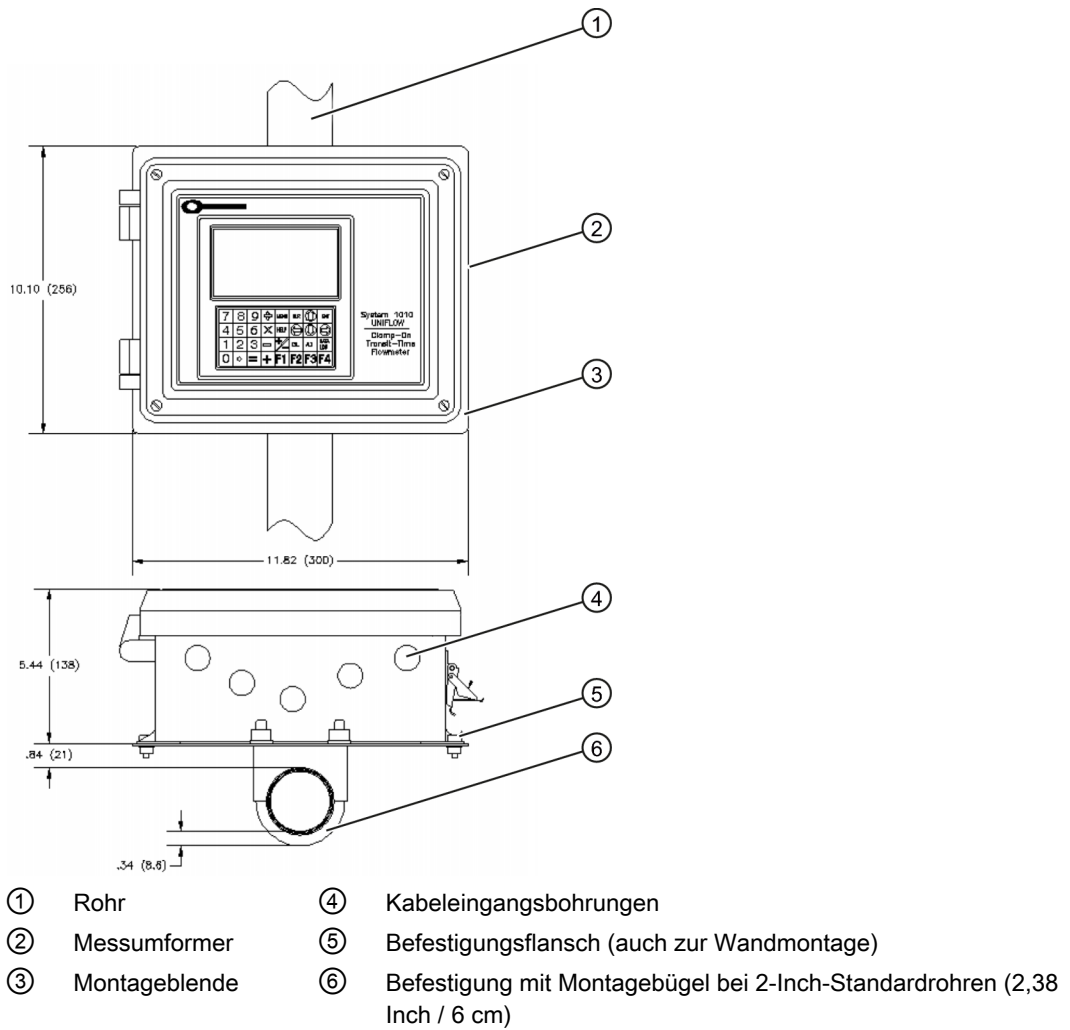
Rohrmontage und Einbauorte des Messumformers
